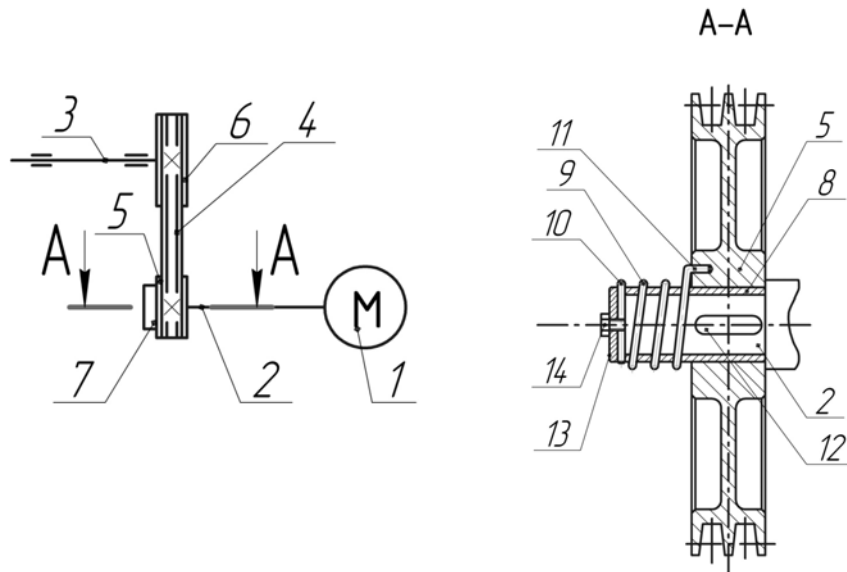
Кінематична схема привода основов'язальної машини з пружною муфтою з циліндричною пружиною кручення
